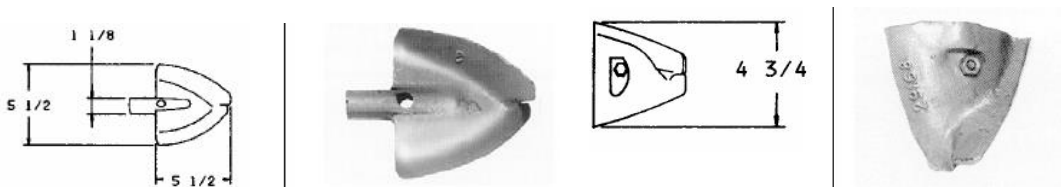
Herramienta de perforación Punta Inferior (Stinger). Pilas en Tobas
